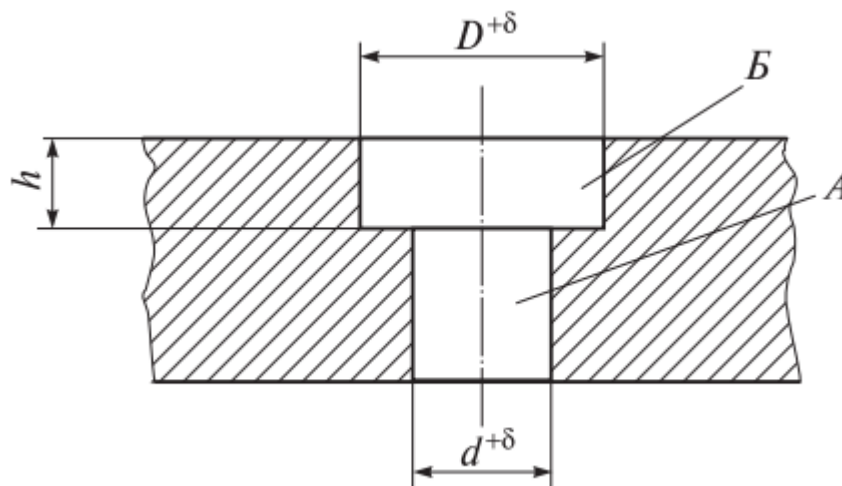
Варіант типового поєднання елементарних поверхонь
